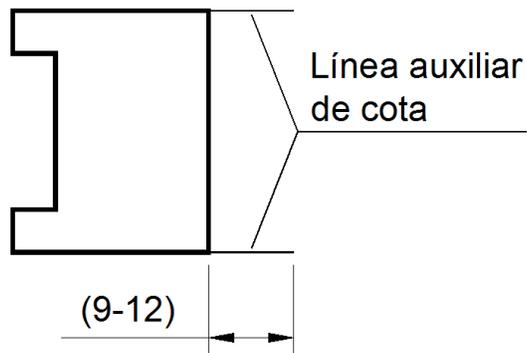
Dimensiones de las líneas auxiliares de cota.
